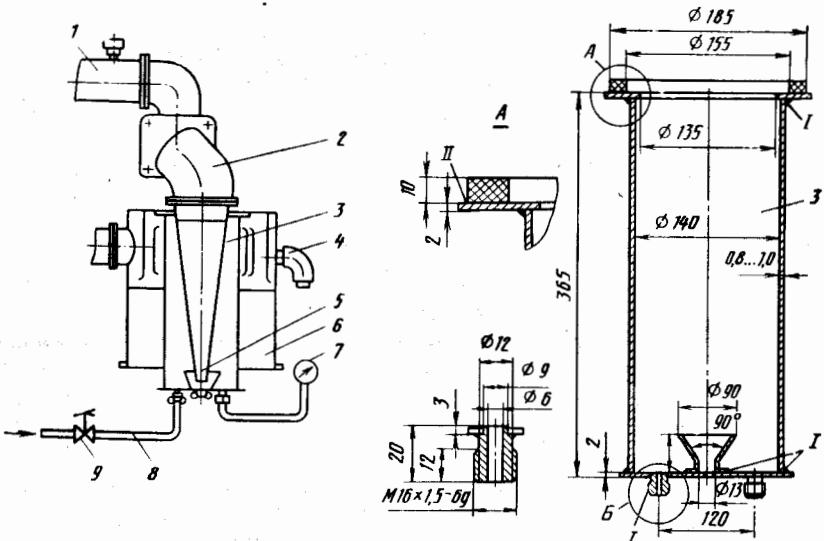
Установка для проверки герметичности впускного тракта от воздушного фильтра к двигателю и рабочий чертеж заглушки:
